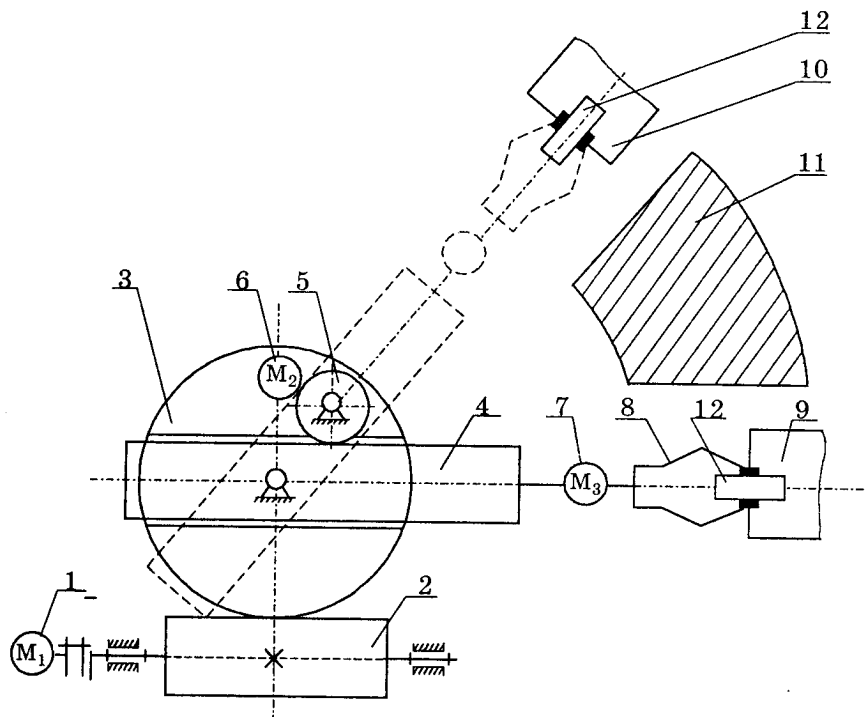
Схема простейшего манипулятора с тремя исполнительными механизмами: 1 — приводной двигатель первого исполнительного механизма (ИМ-1); 2 — червяк; 3 — червячное колесо; 4 — рейка, перемещающаяся в направляющих червячного колеса; 5 — приводная шестерня; 6 — двигатель второго исполнительного механизма (ИМ-2); 7 — двигатель привода схвата 8 третьего исполнительного механизма (ИМ-3); 8, 9, 10 — транспортеры; 11 — неподвижный объект, расположенный между транспортерами; 12 — транспортируемая деталь
